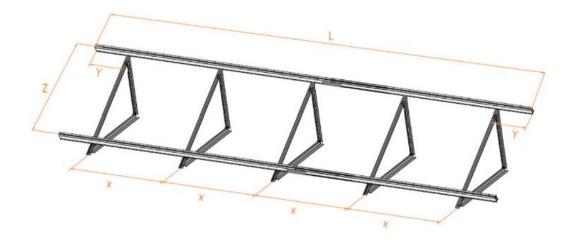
Informe sobre las dimensiones de la estructura proyectada (Fuente: SOLARSTEM).
